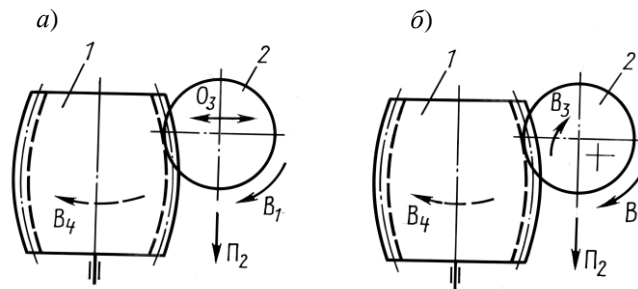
Схемы формообразования бочкообразных зубьев с реверсивным относительным движением инструмента (а); с планетарным движением инструмента (б)
